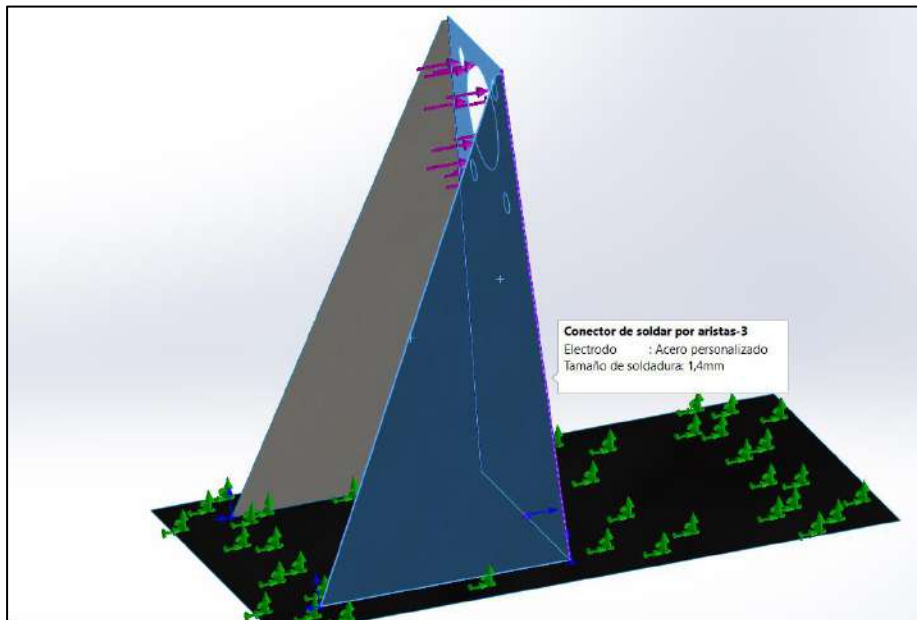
Adición de soldadura en las cartelas.
